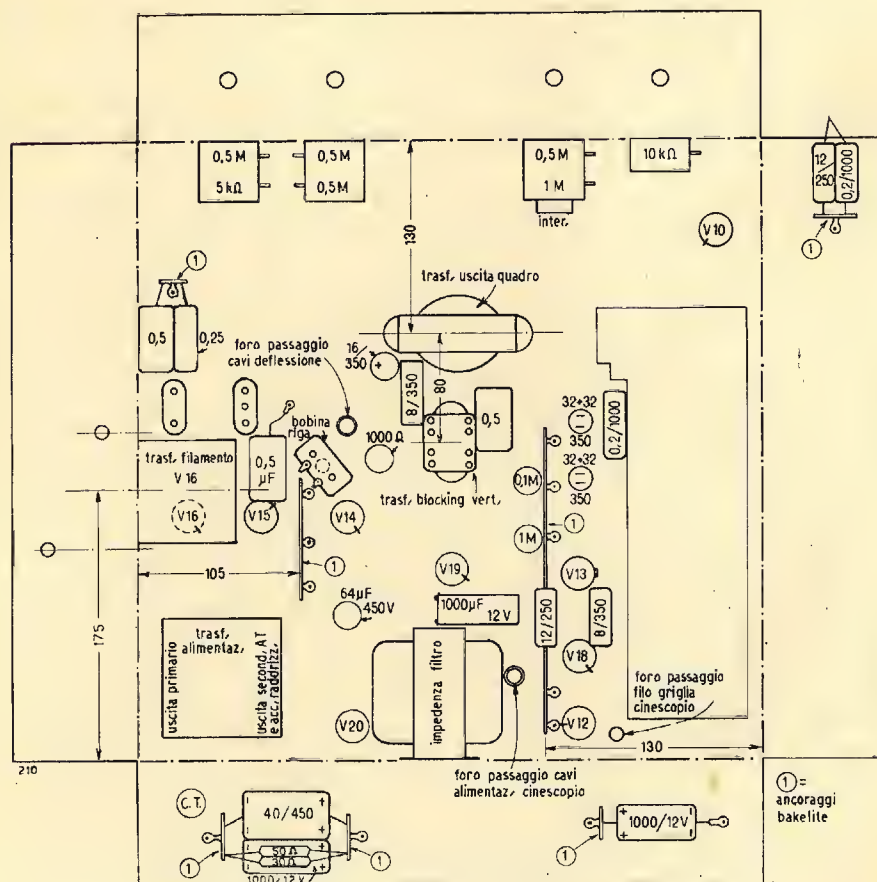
Disposizione di montaggio componenti sullo chassis.
